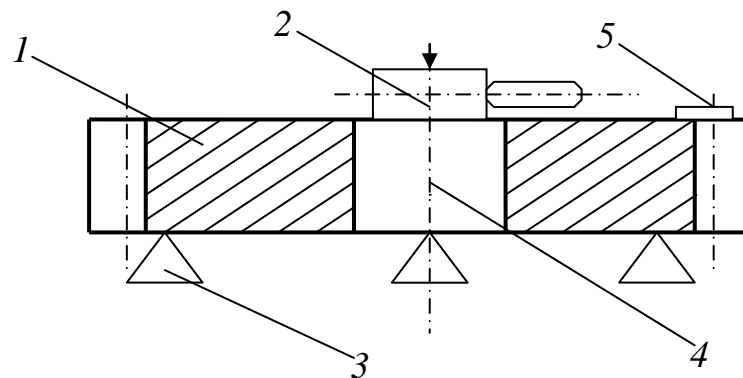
Схема установки крупногабаритного зубчастого колеса:
